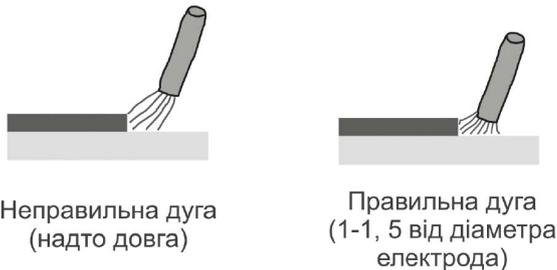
Відстань розташування електрода із покриттям до деталі під час ручного дугового зварювання («ММА»).
